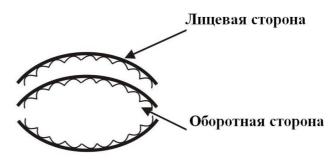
Схема сборки пакета из листов шпона трехслойной фанеры
